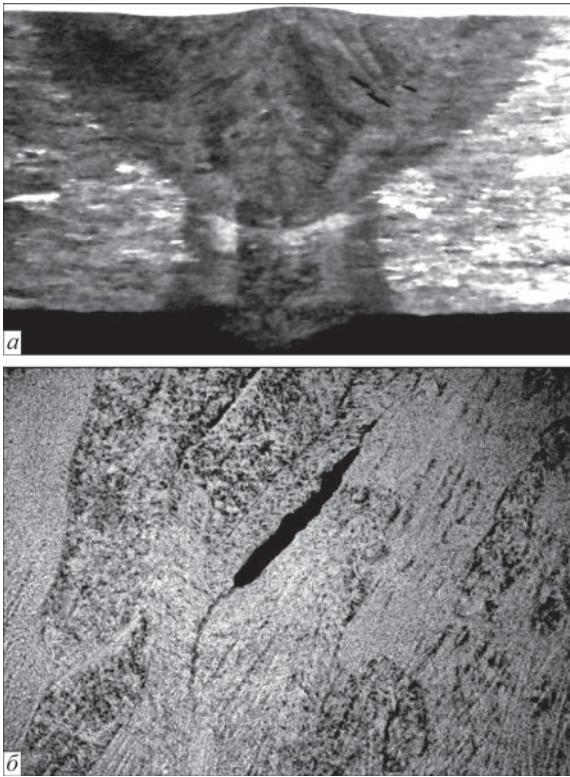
Структура образца № 3: *а* — поперечный макрошлиф сварного соединения; *б* — участок шва с трещиной ($\times 500$)
